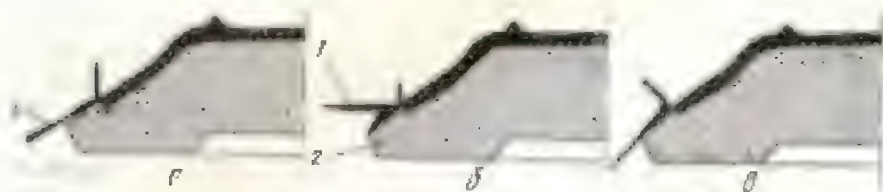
Установка ножа приспособления для срезания избытка массы у края изделия
